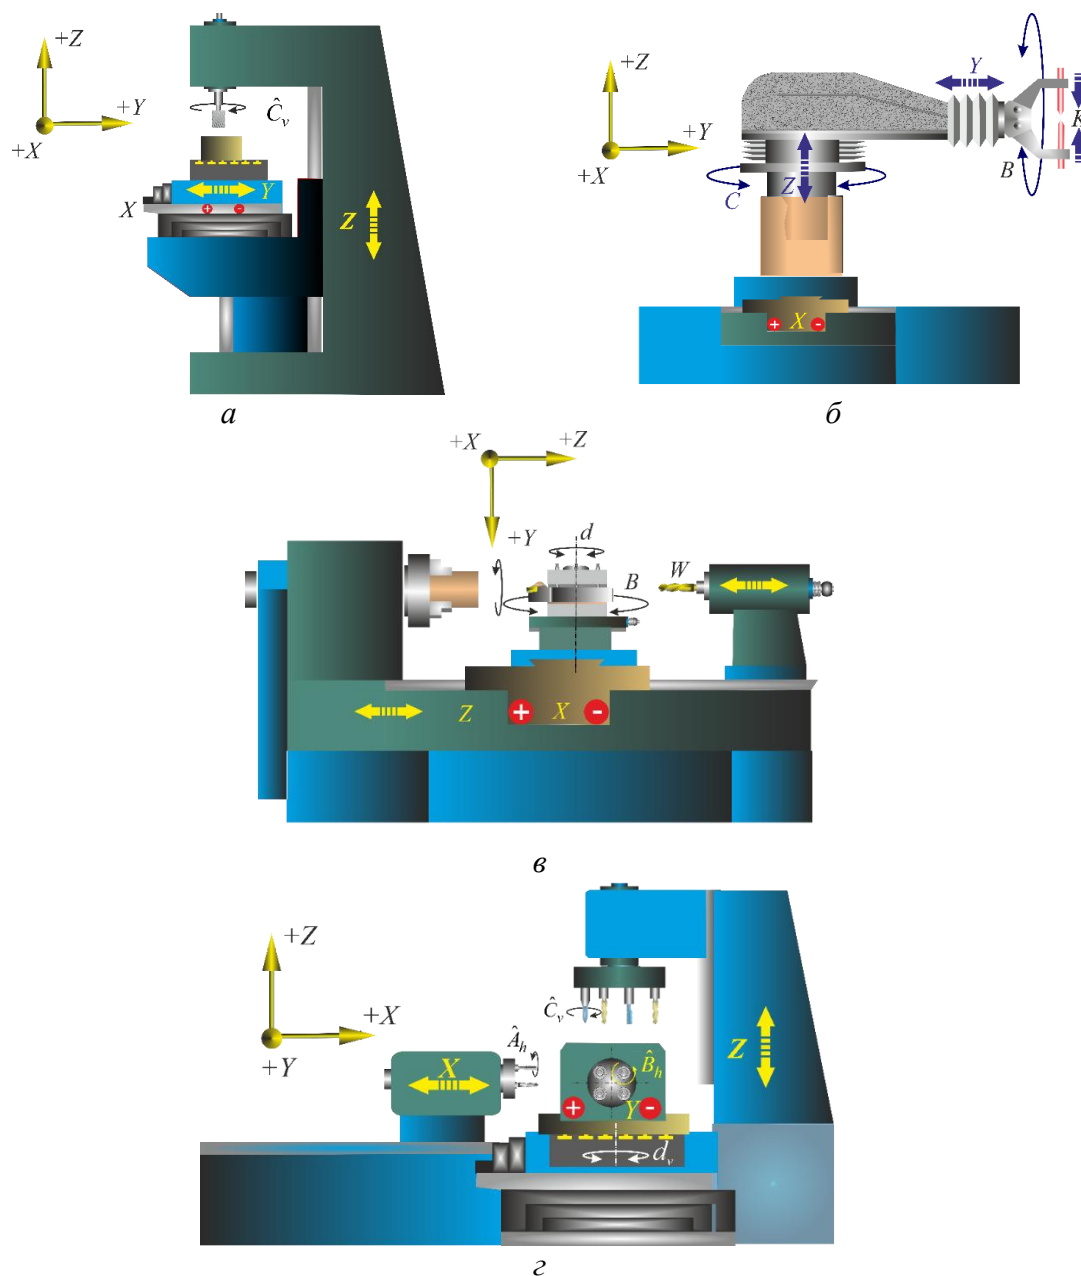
Компоновка технологического оборудования с указанием координатных осей и движений: *a* – фрезерного станка; *б* – промышленного робота; *в* – токарного станка; *г* – агрегатно-сверлильного станка
